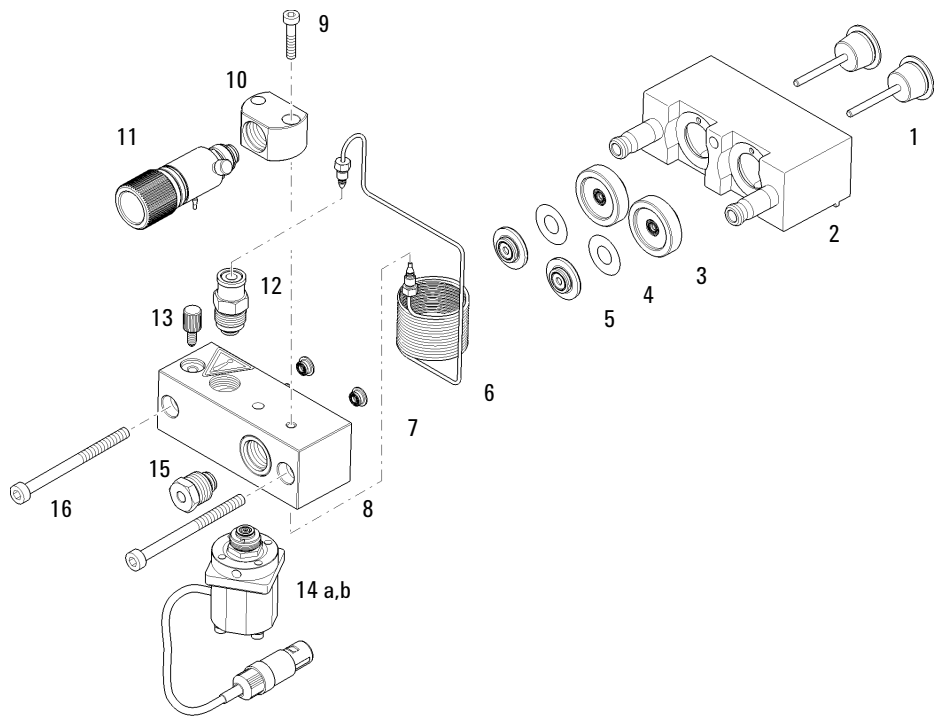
Ensemble tête de pompe sans accessoire de rinçage des joints
